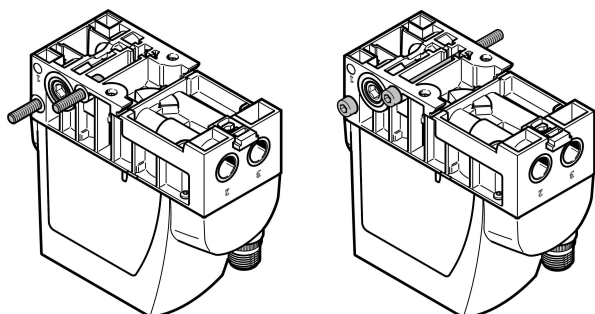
Befestigung über Seitenfläche mit innenliegenden Schrauben M4/durchgehenden Schrauben M4
